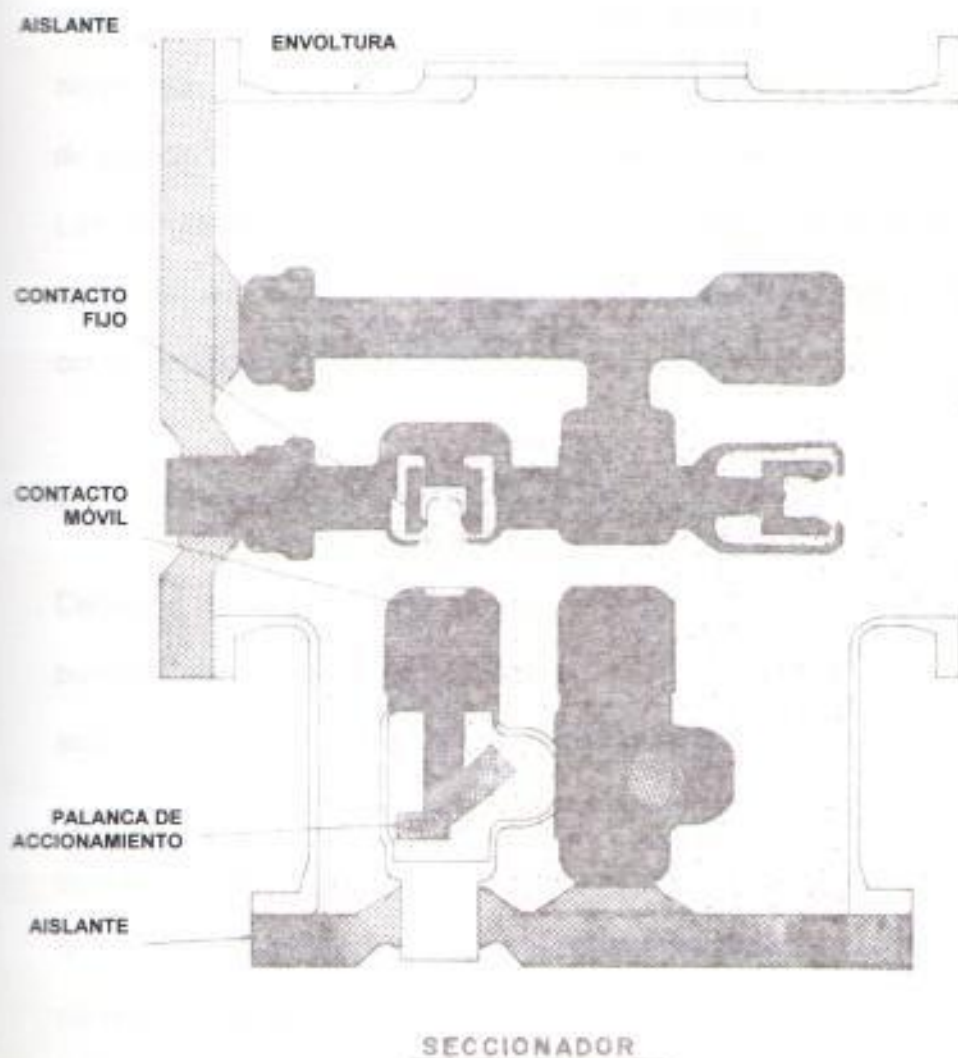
Esquema interior del seccionador de una posición encapsulada
